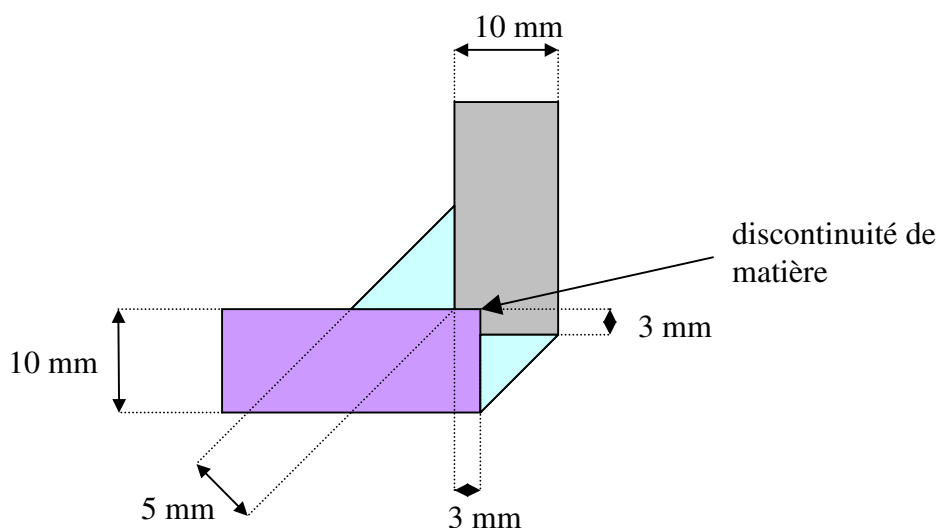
géométrie de la soudure en L entre le plancher et la paroi latérale
